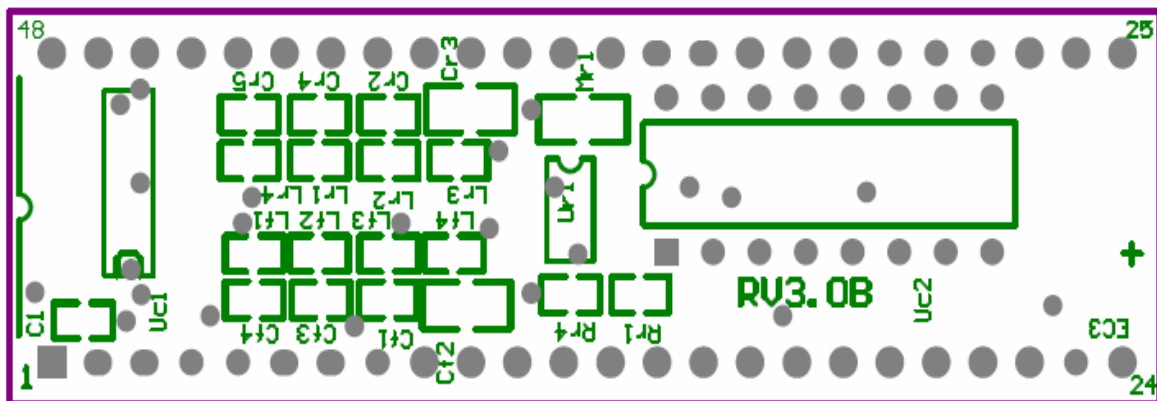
SRFC—I 型控制模块上层 PCB 板丝网印刷图
